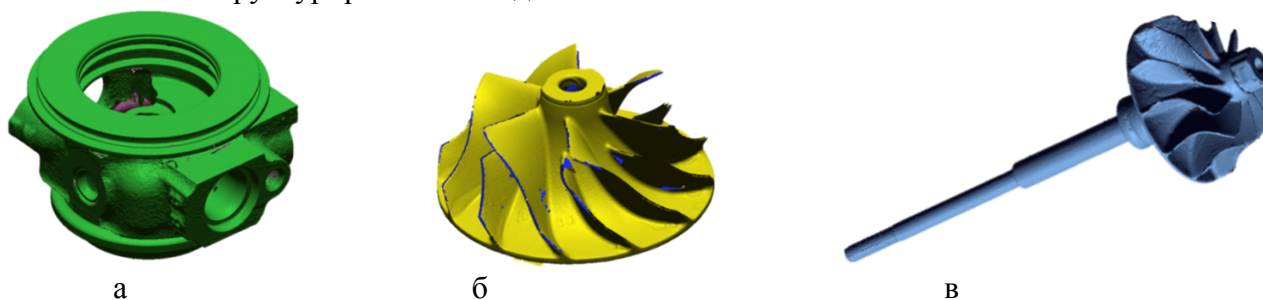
Сканы деталей турбокомпрессора: а – корпус, б – колесо, в -вал
